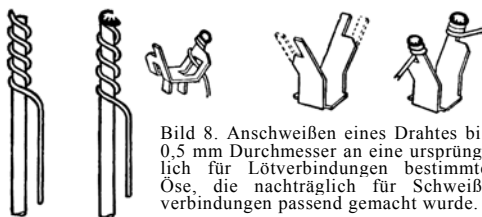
Anschweißen eines Drahtes bis 0,5 mm Durchmesser an eine ursprünglich für Lötverbindungen bestimmte Öse, die nachträglich für Schweißverbindungen passend gemacht wurde.
